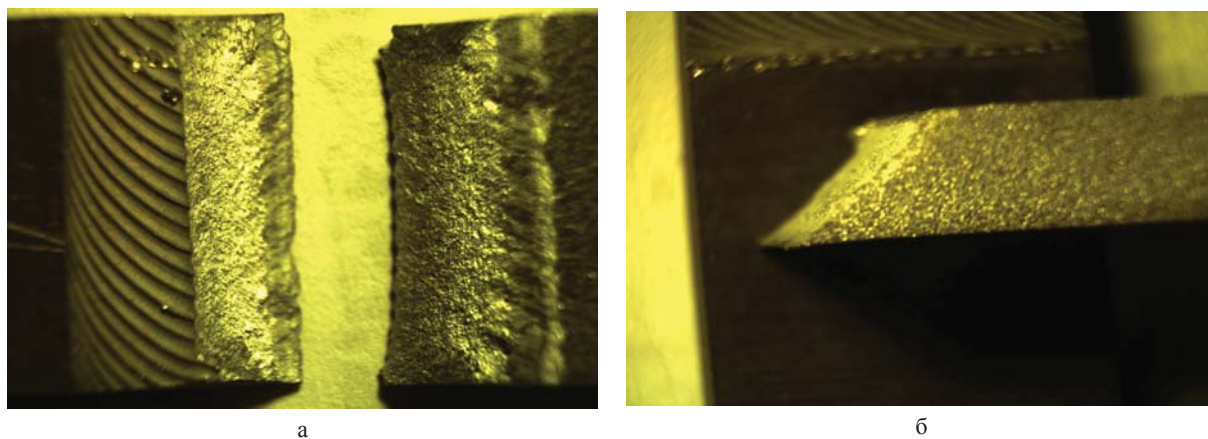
Разрушенный образец со сварным соединением (режим 1): а — вид сверху; б — вид сбоку
